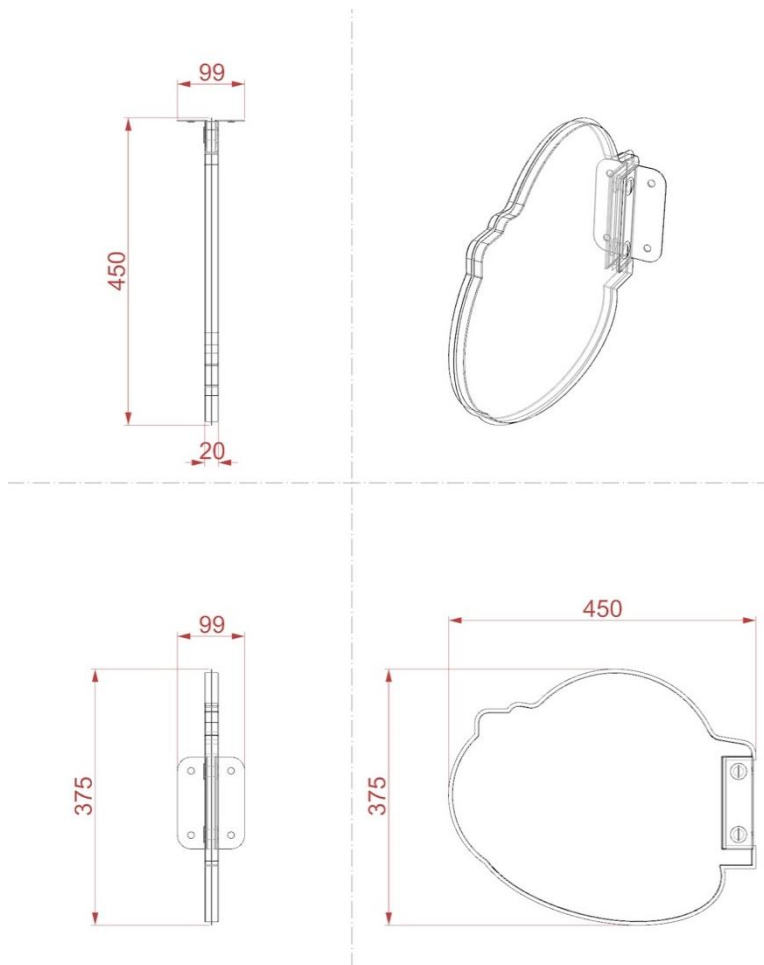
2 - Dibujo técnico y medidas generales del flanger
